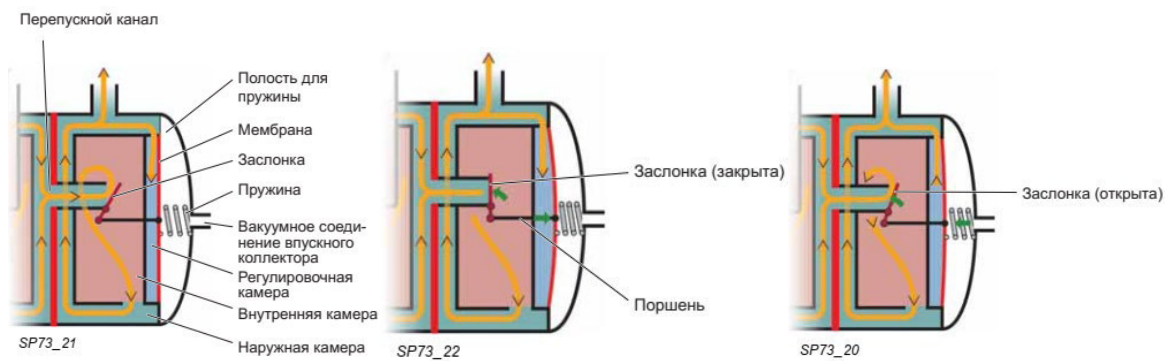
Схема роботи другої ступені газового редуктора-випарника
